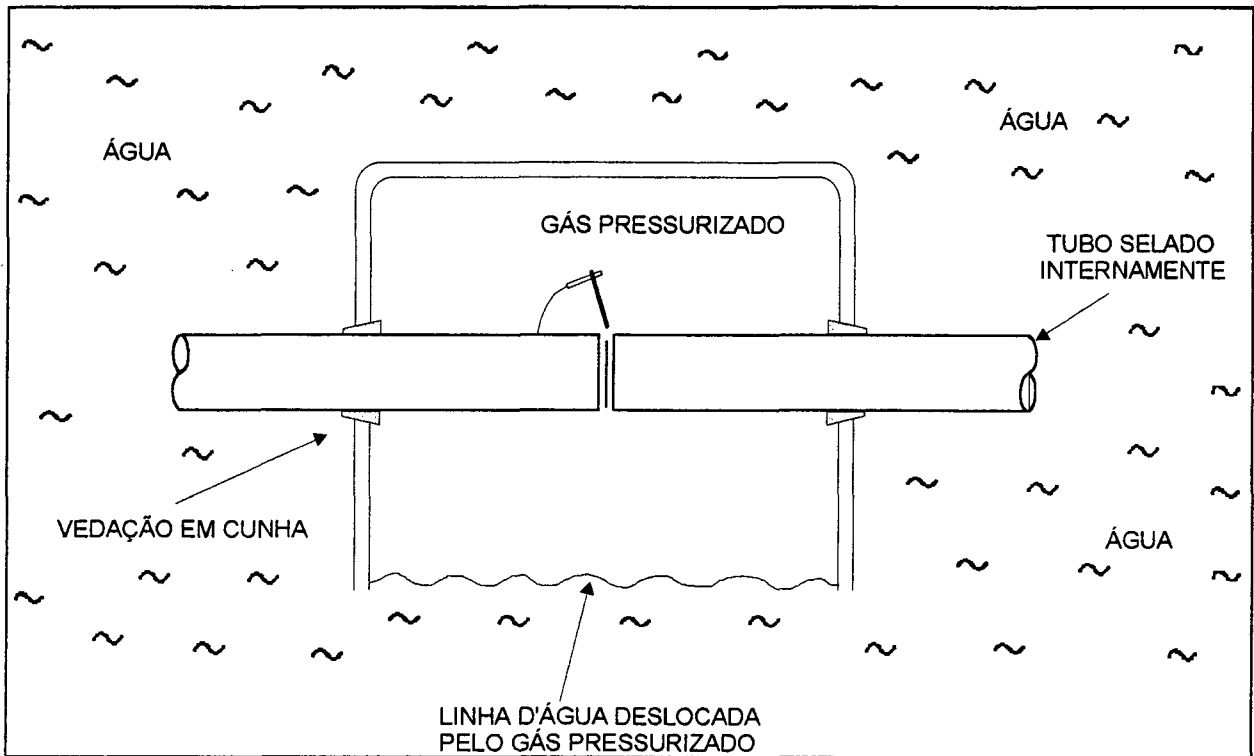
Técnica da soldagem subaquática hiperbárica [8].
